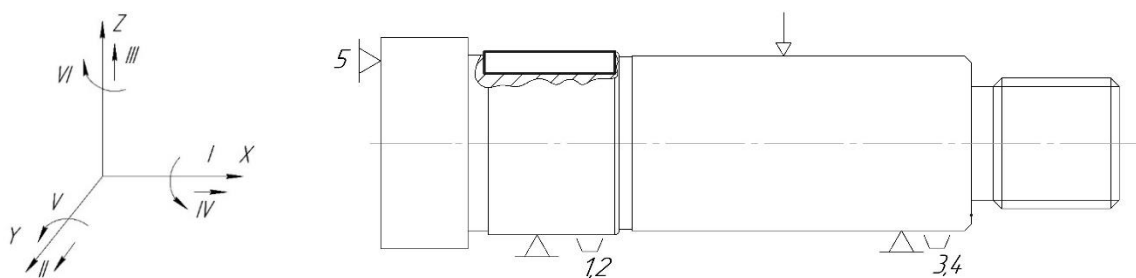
Схема базування та закріплення заготовки на операцію 030 Вертикально-фрезерну з ЧПК
